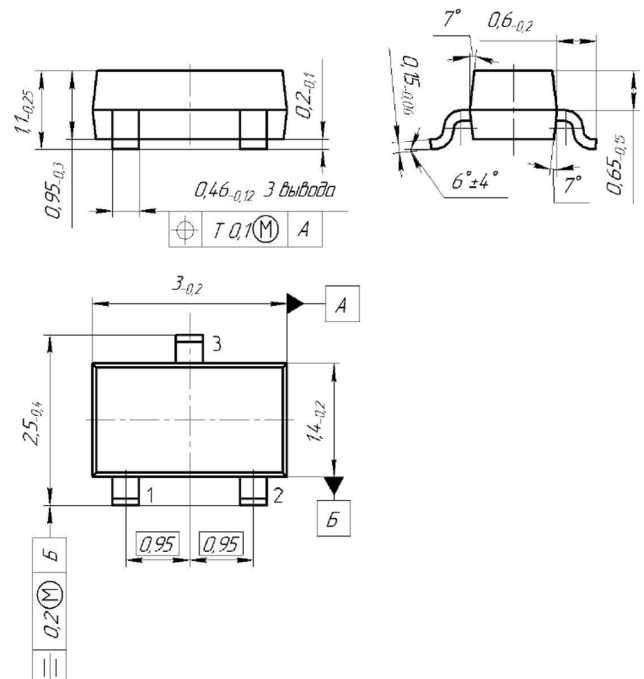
Габаритный чертёж корпуса КТ-46.
